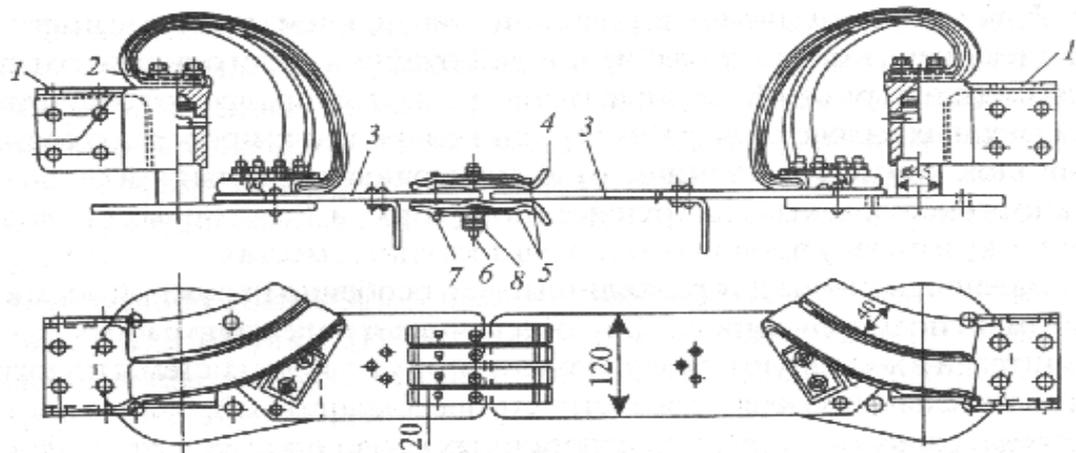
Токоведущая система горизонтально-поворотного разъединителя:
